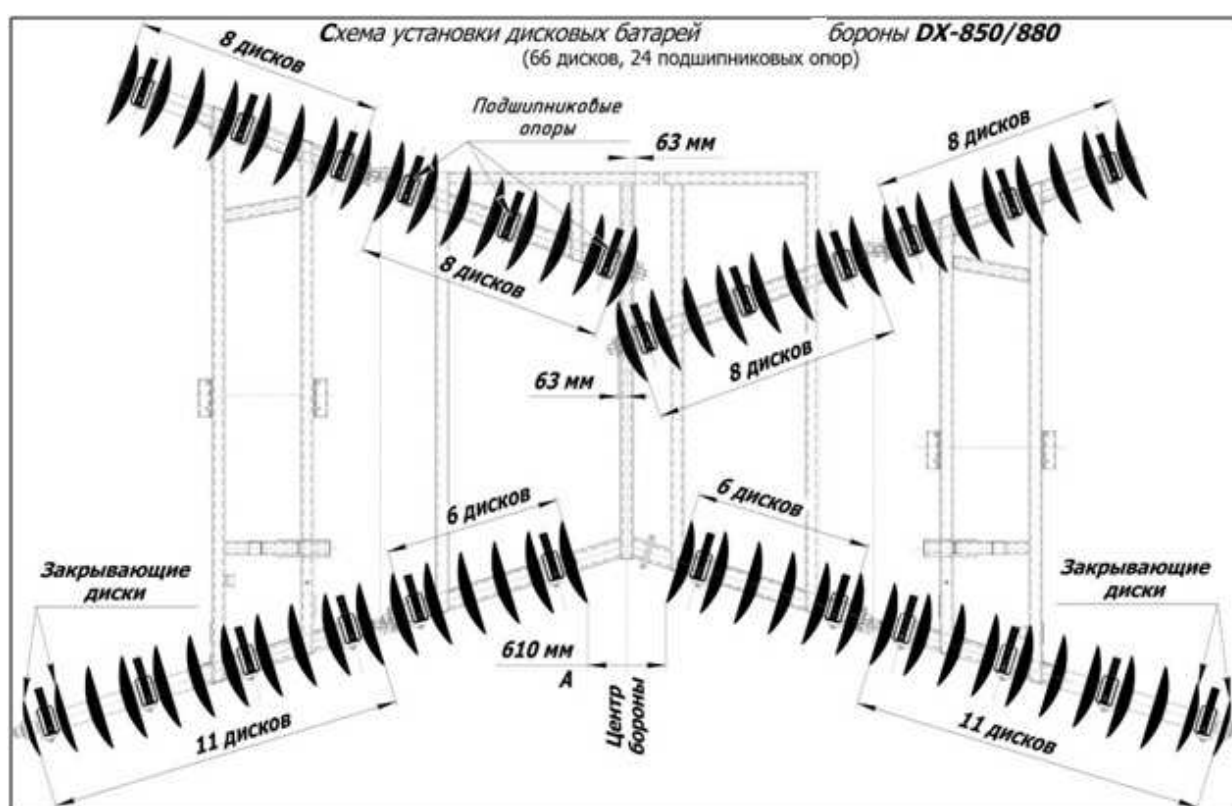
Схема установки дисковых батарей для бороны DX-850/880
